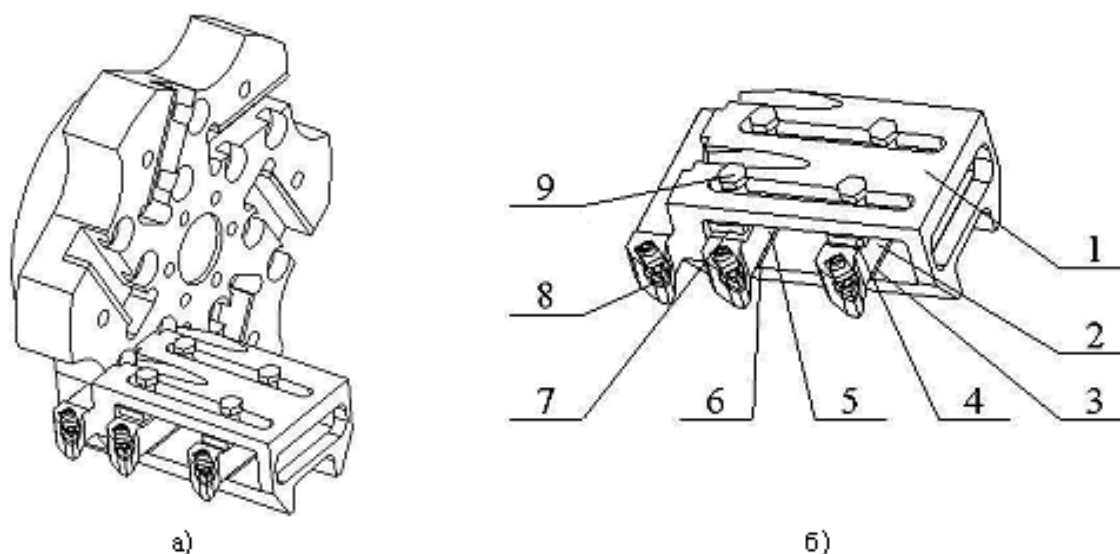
Багаторіцева державка: а – схема закріплення у пазу револьверної інструментальної головки токарного верстата з ЧПК; б – загальний вигляд багаторіцевої державки
